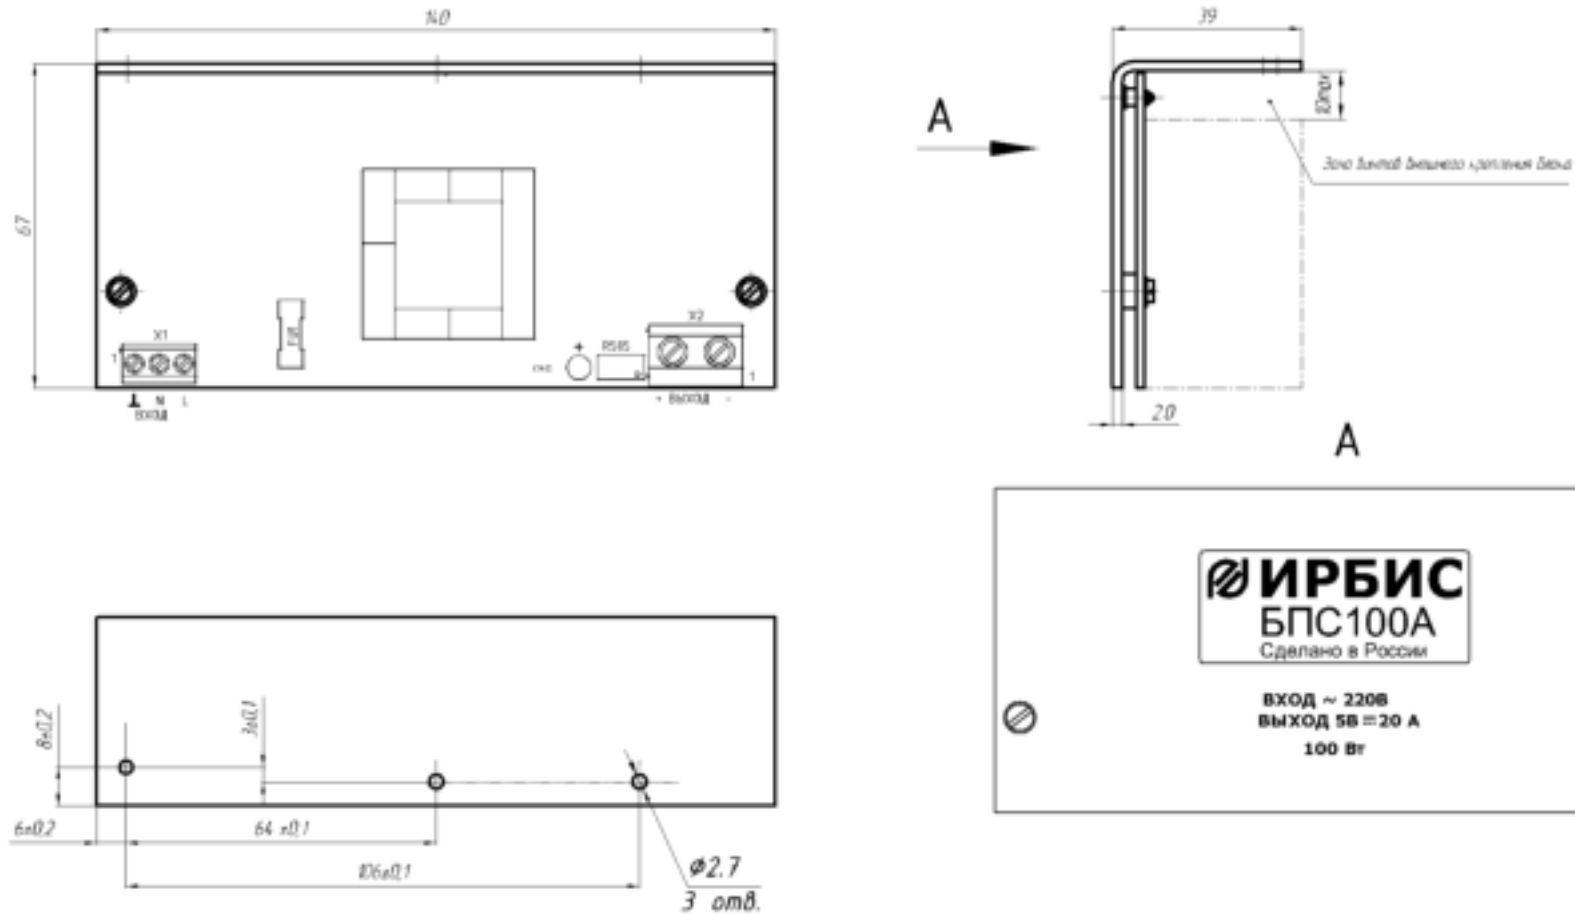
Габаритный чертеж модуля питания БПС100
